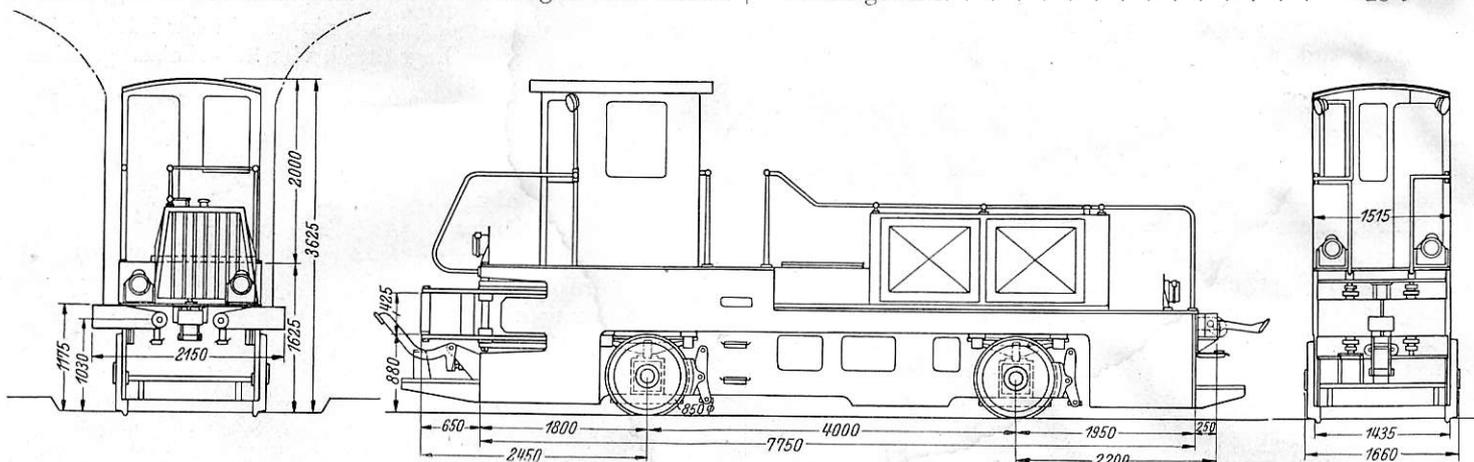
Rangiergerät mit seitlich ausschwenkbarer Zug- und Stoßvorrichtung.
